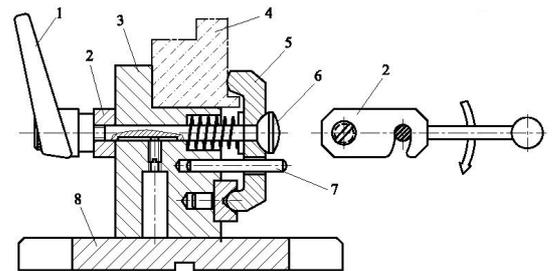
Fräsvorrichtung mit Schwenkscheibe als Spannelement
